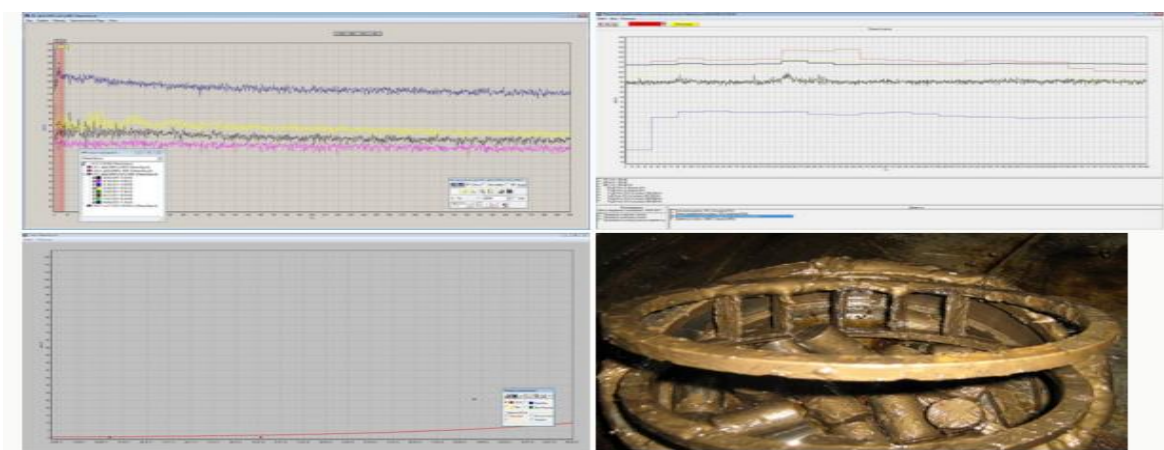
Вибрация буксы колесной пары, в одном из подшипников в котором разрушен сепаратор
